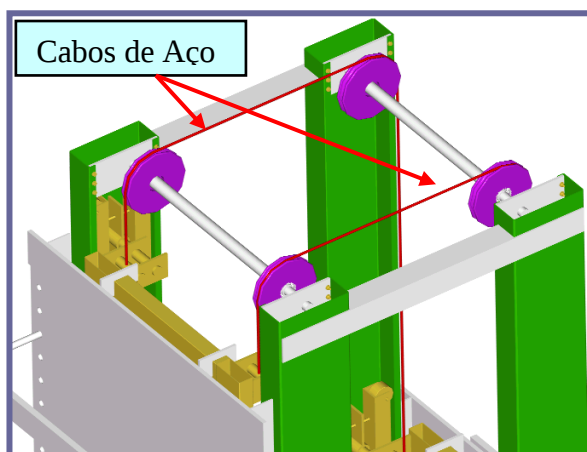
Cabos de Aço da parte superior do equipamento de movimentação vertical.
